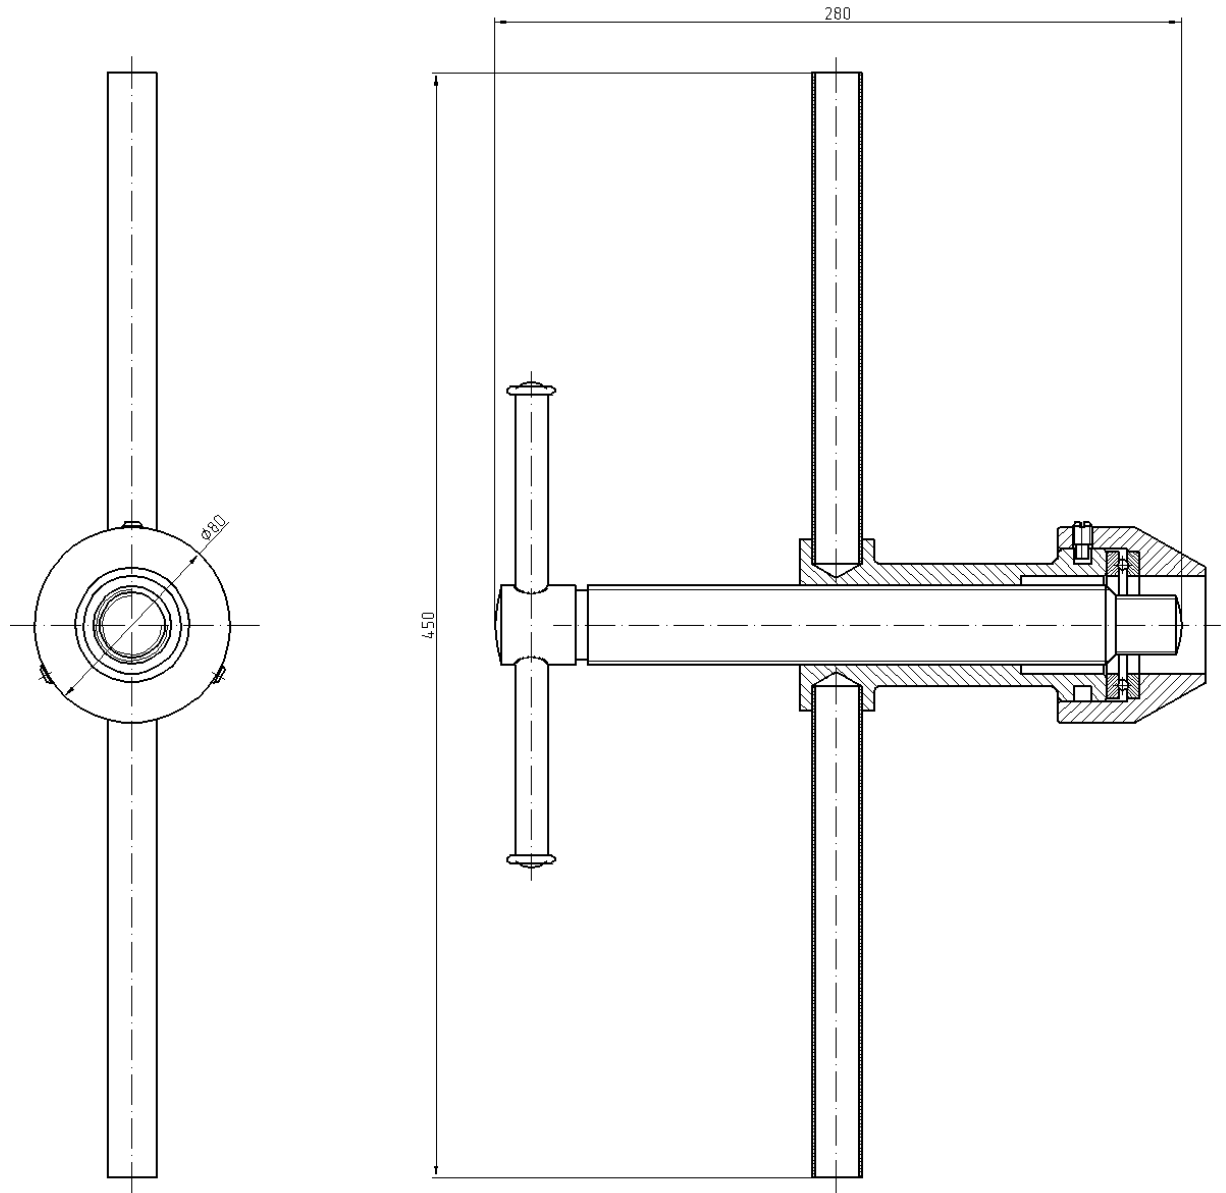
ЗМ 7823-4291-01 – Приспособление для напрессовки звездочки и ступицы на коленчатый вал
